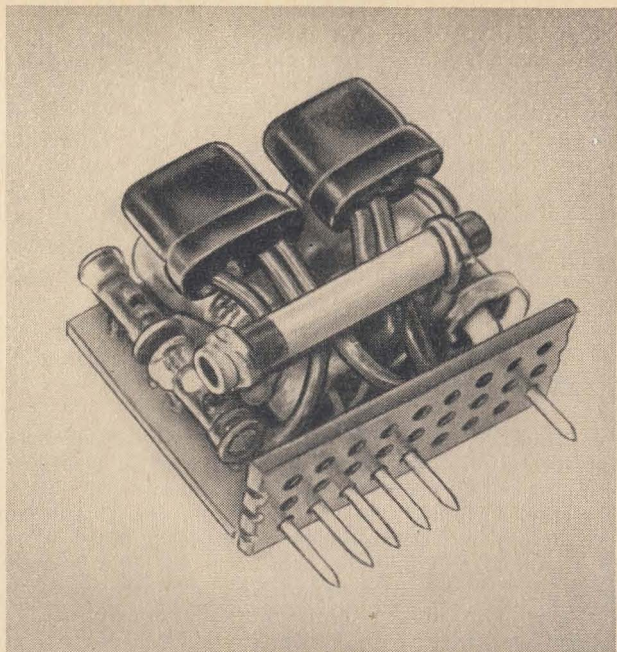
Baugruppe mit unbestückter Lochleiste als unterem Abschluß
